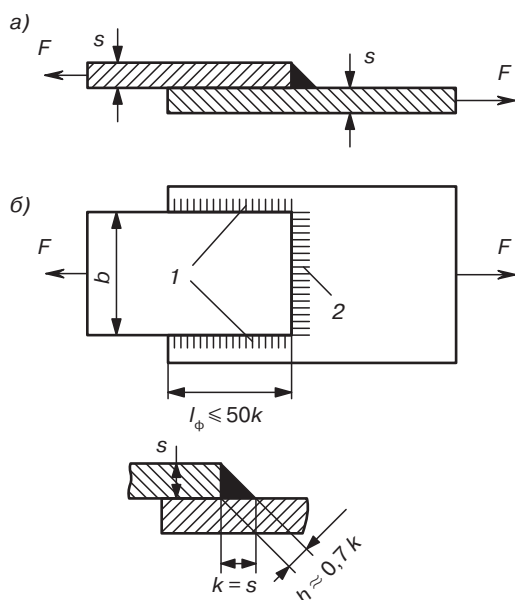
Сварное соединение внахлестку: а — комбинированный сварной шов (1 — фланговые, 2 — лобовой); б — угловой шов
